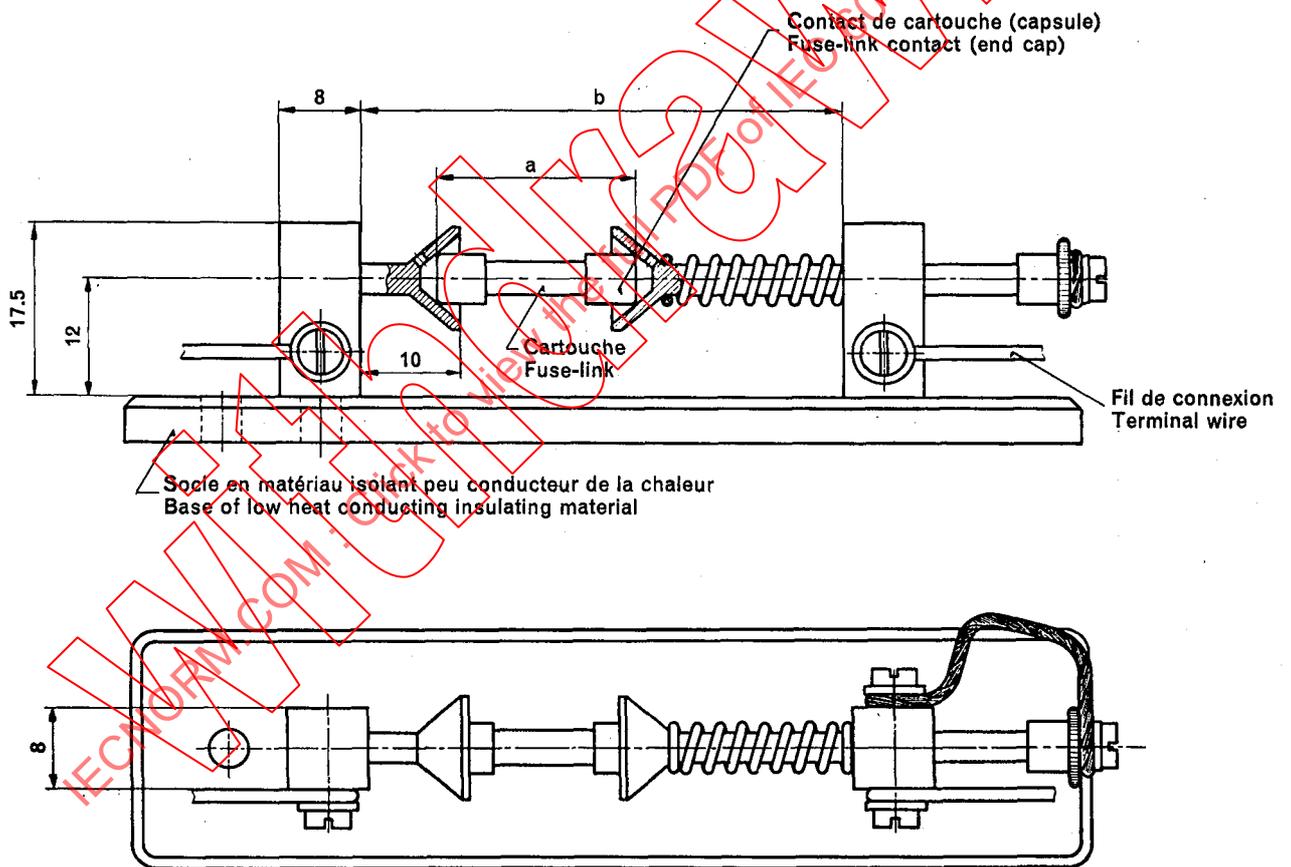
Socle d'essai pour cartouches 5 mm × 20 mm et 6,3 mm × 32 mm.
